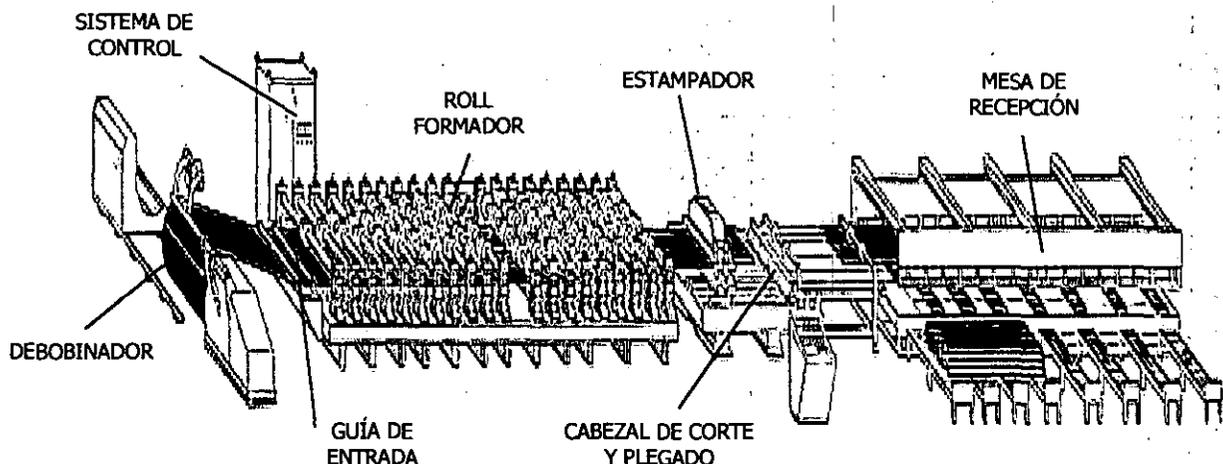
Diseño básico de una Línea de Conformado por Roll Forming.
